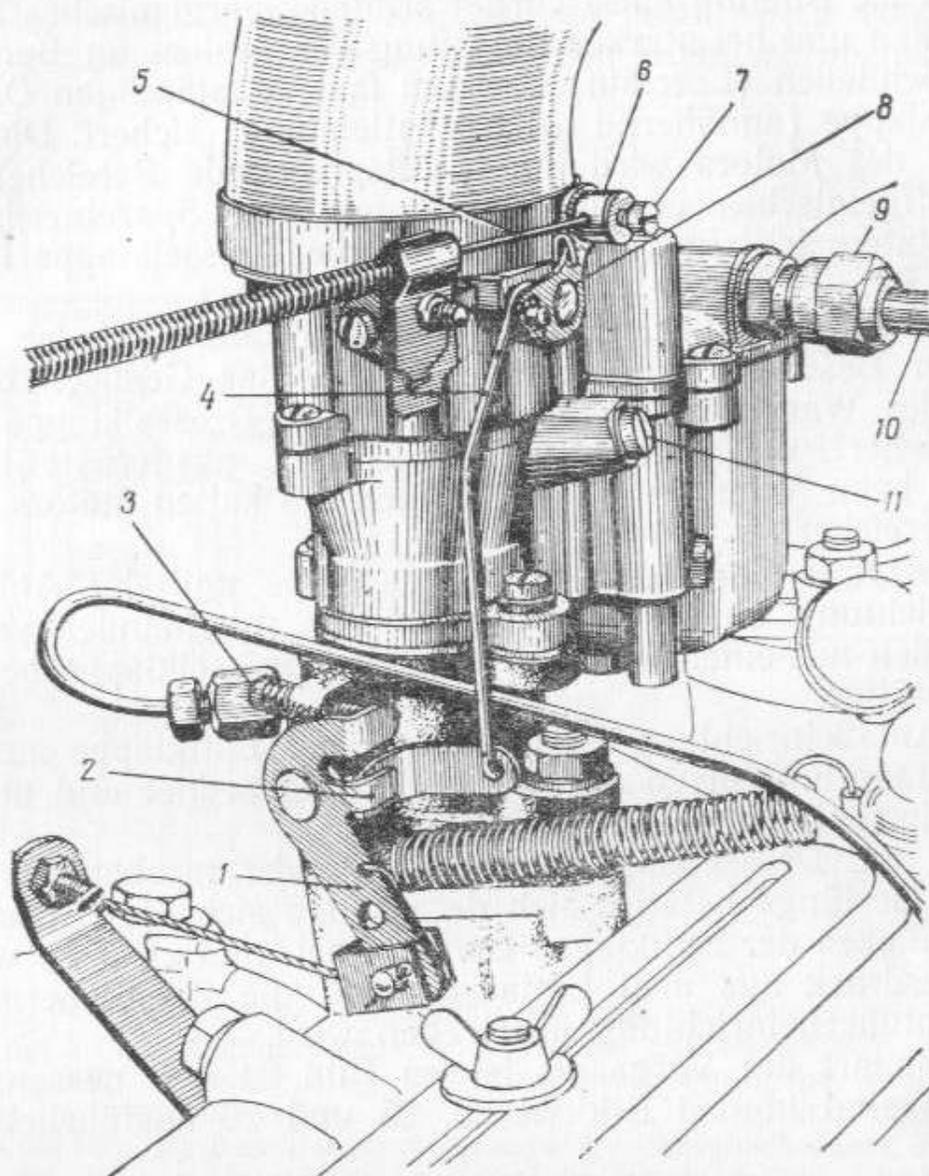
Gesamtansicht des Vergasers Typ K-59, schräg von hinten gesehen:
